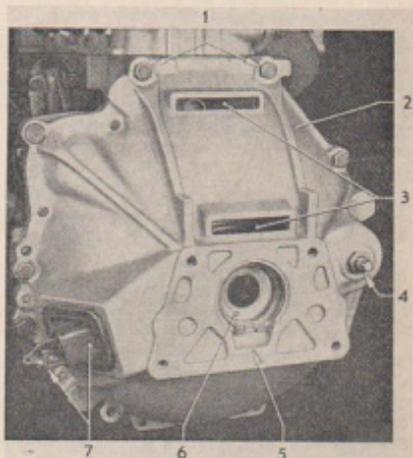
Kupplungsgehäuse an Motorblock geschraubt
